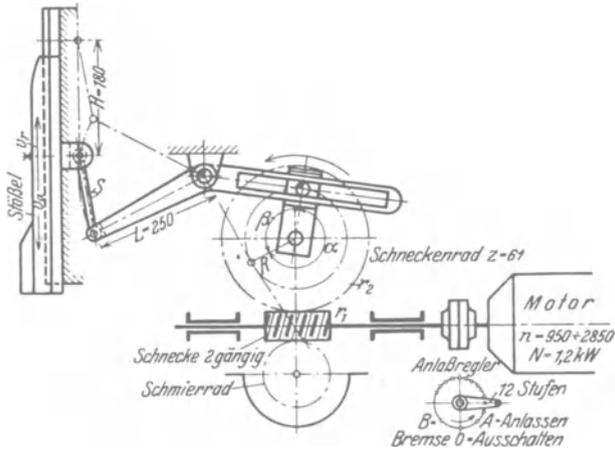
Antrieb der Stoßmaschine mit regelbarem Motor.
